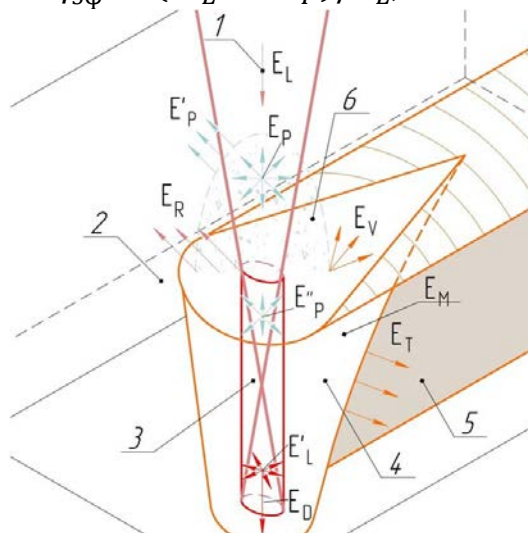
схема энергетического баланса лазерной сварки [8]: 1 – сфокусированный лазерный луч; 2 – основной металл; 3 – кинжальное проплавление; 4 – жидкий металл; 5 – сварной шов; 6 – рассеивающиеся пары металла.
